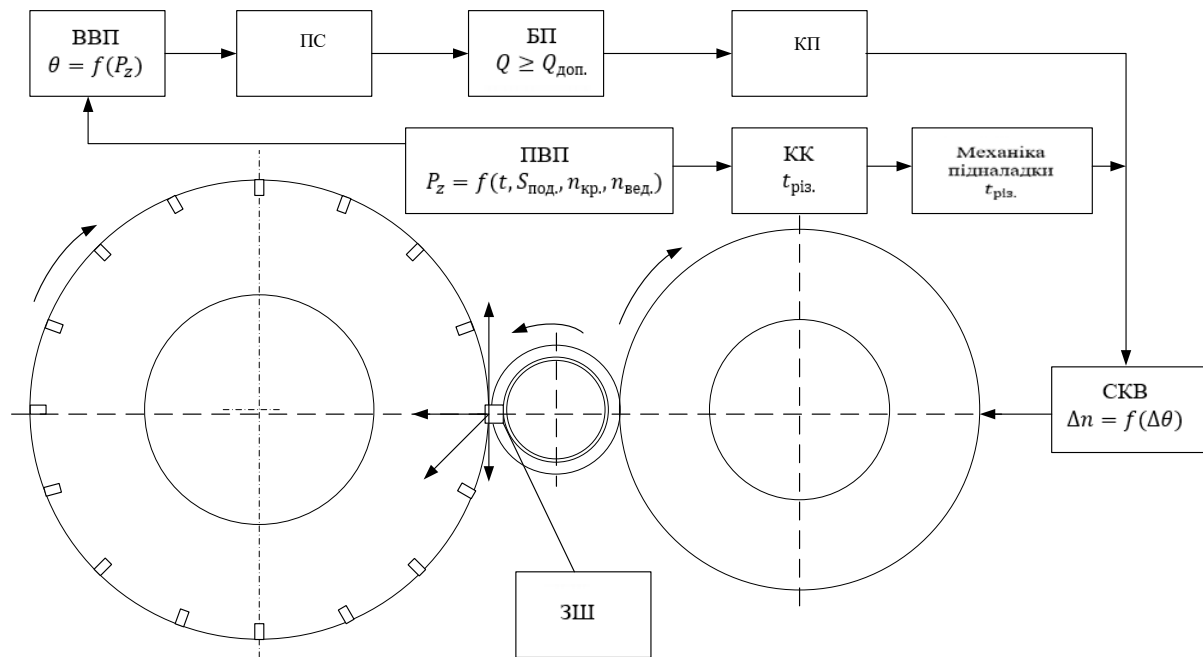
Система адаптивного бездефектного шліфування на базі безцентрово-шліфувального верстату SASL5AD: 1 – шліфувальний круг; 2 – заготовка; 3 – ведучий круг; ЗШ – зона шліфування; ПВП – первинний вимірювальний перетворювач; ВВП – вторинний вимірювальний перетворювач; ПС – підсилювач сигналу; БП – блок порівняння; КП – керуючий прилад; КК – контролер керування; СКВ – система керування верстатом; Δn – зміна частоти обертання ведучого круга, яка необхідна для забезпечення потрібного значення тангенціальної сили ΔP_z ; $\Delta \theta$ – регульована температура; $t_{\text{різ.}}$ – глибина шліфування
